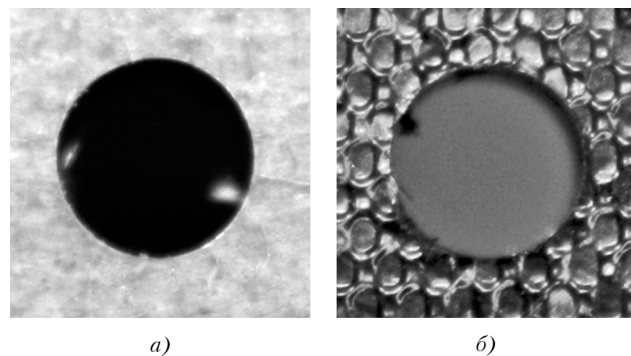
Качество кромок отверстий, выполненных сверлами Guhring 704 с использованием СМАП модели PFD1500, в деталях из ПКМ: а) — со стороны входа сверла в пакет; б) — со стороны выхода сверла из пакета
